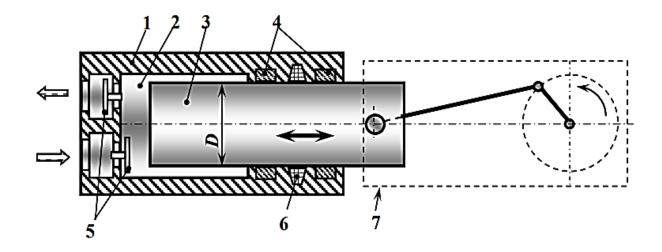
Схема плунжерного насоса с кривошипно-шатунным приводом: 1 — цилиндр; 2 — рабочая полость цилиндра; 3 — плунжер; 4 — направляющие подшипники скольжения; 5 — самодействующие клапаны; 6 — сальник (уплотнение); 7 — механизм привода плунжера
